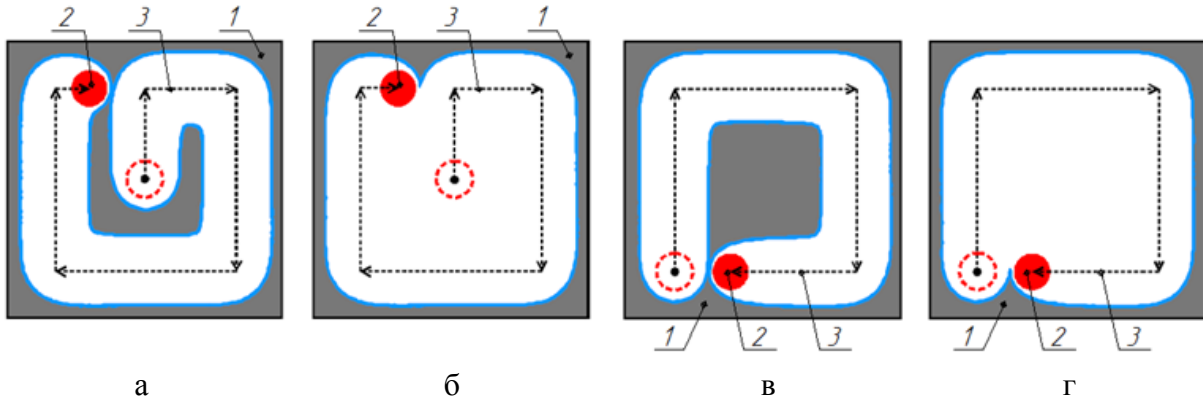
Геометрия реза до (а, в) и после (б, г) взаимопересечения (топологического изменения) обрабатываемой поверхности для различных траекторий перемещений ПЭИ. Безразмерный межэлектродный зазор равен 0.1
